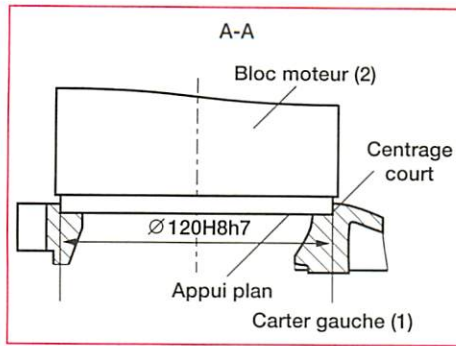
Positionnement par appui plan et centrage court (coupe A-A)
